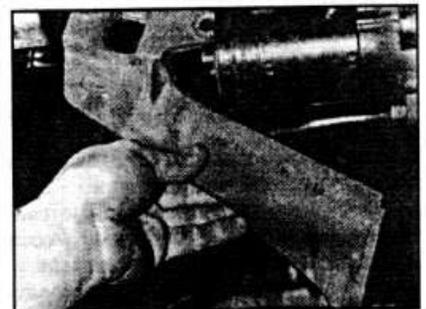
В.43. Болты вспомогательной подвески со стороны стартера - двигатель 1,6 дм³.
